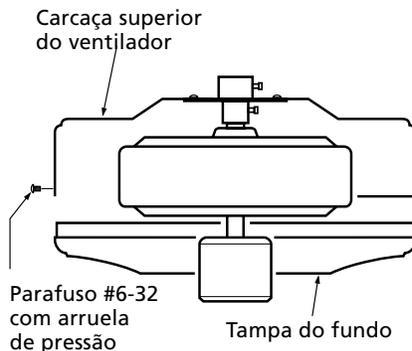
Fixando a tampa do fundo à carcaça superior do ventilador
